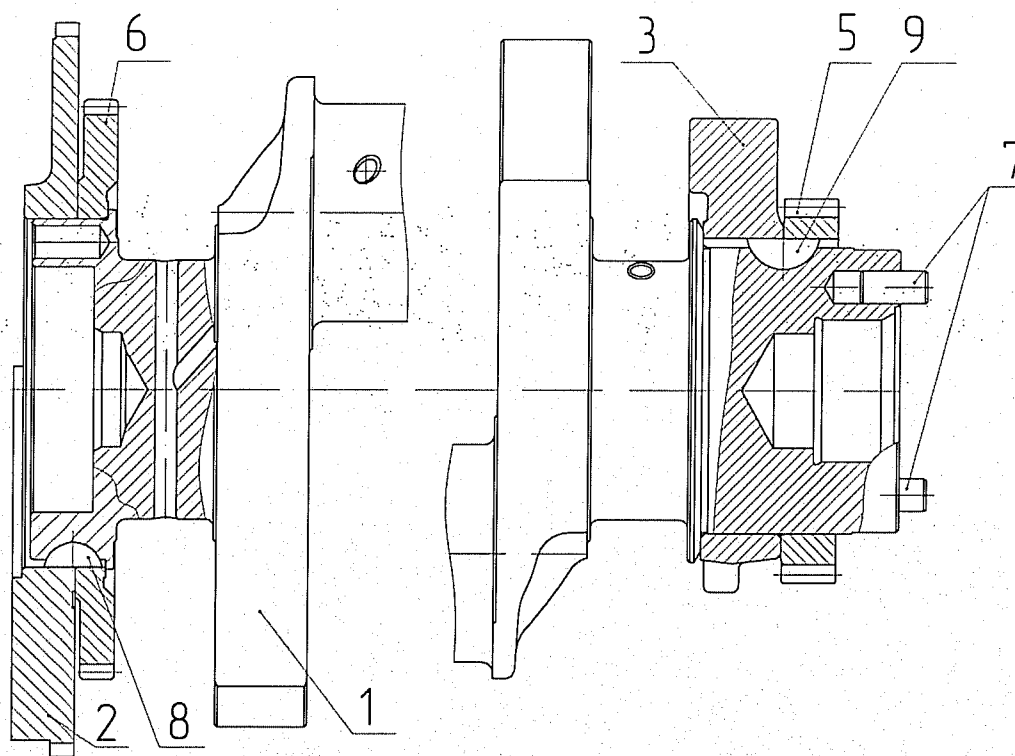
Сборочный чертеж коленчатого вала двигателя 740.65-240, собранного на базе вала 740.65-1005020
